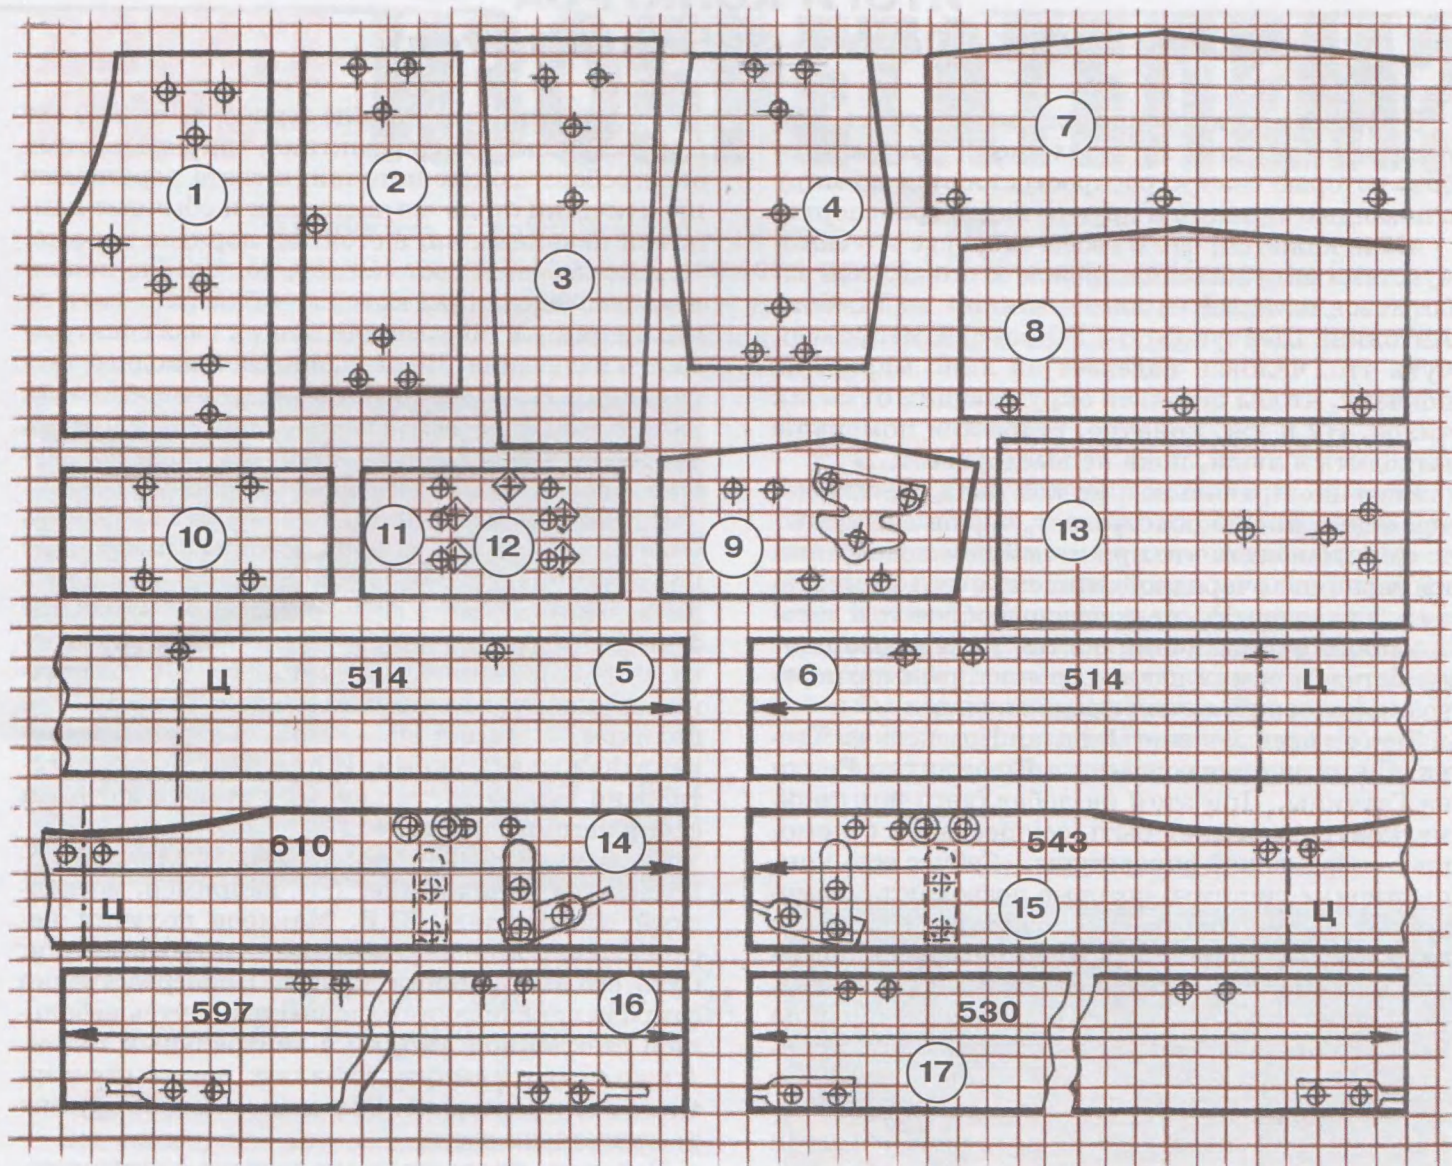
Развертки корпусных деталей доспеха (номера деталей соответствуют номерам на рисунке 1). Клетка 15x15 мм, обозначения центров отверстий в ромбе — только для детали 12. Обозначения центров отверстий в кружке или пунктиром относятся к противоположной стороне деталей 14 и 15.
